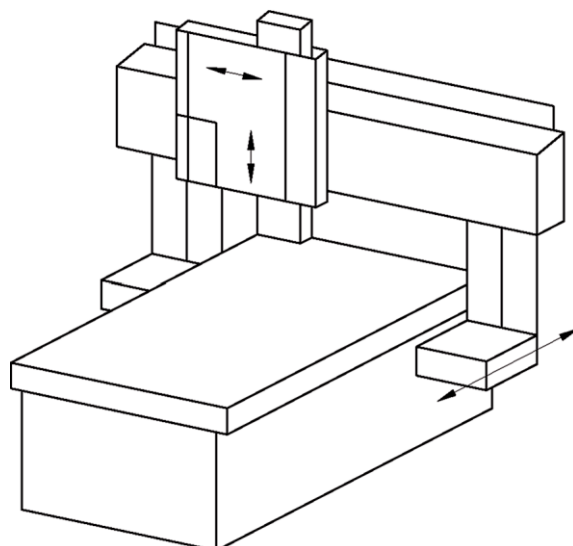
Exemple de machine à portique avec table fixe, portique mobile, tête d'usinage mobile
